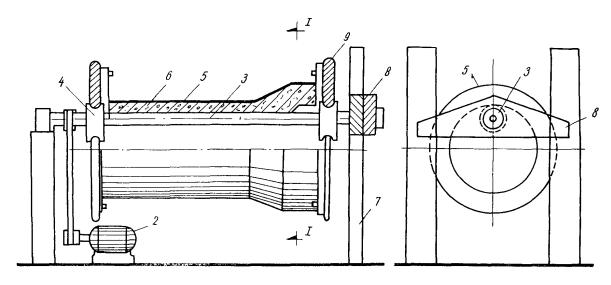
Схема центробежной прокатной машины I — опора; 2 — привод; 3 — вал; 4 — каток с ребордой; 5 — форма; 6 — труба; 7 — стойка; 8 — траверса для крепления вала; 9 — торцовая шайба формы
